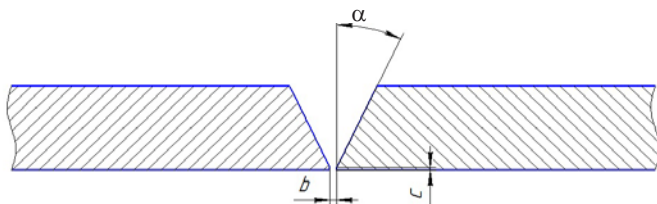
Параметры подготовки и сборки свариваемых пластин: α – угол разделки кромок, град.; b – зазор в стыке, мм; c – притупление, мм
